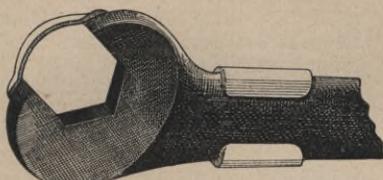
Mit dem Schröderschen Schuttring ausgerüsteter Schraubenschlüssel.
